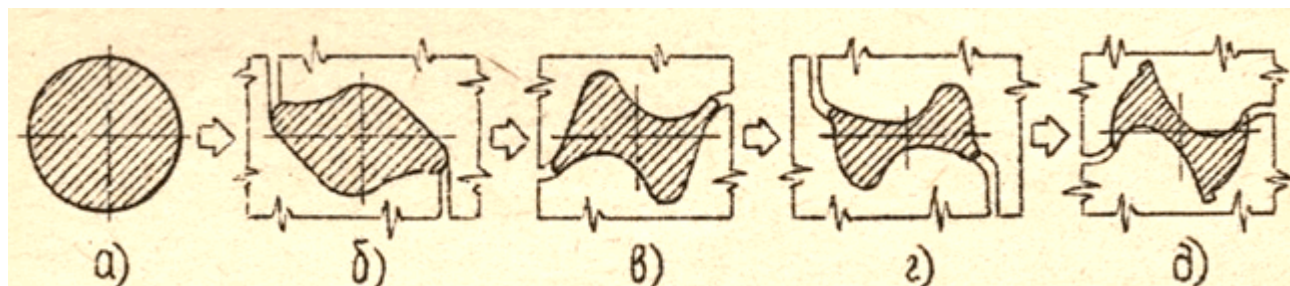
Формоизменение заготовки сверла в ручьях стана секторной прокатки: а — исходная заготовка; б–д — формоизменение заготовки в ручьях стана
